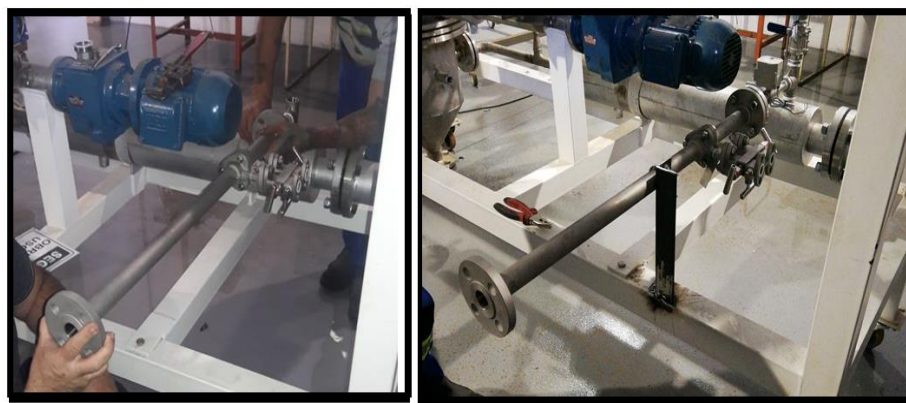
Pré-montagem do orifício integral sobre o superaquecedor.
